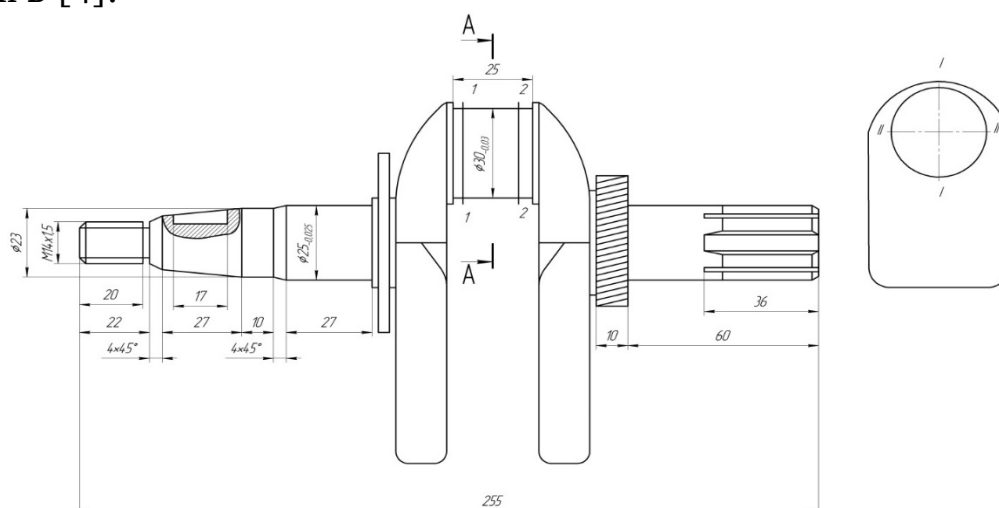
Схема вимірювання колінчатого валу в місцях розміщення шатунного підшипника
